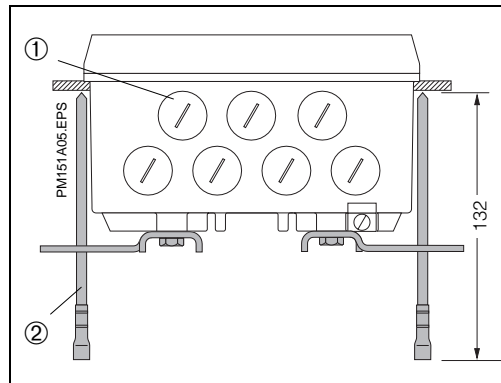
Unterseite des Feldgehäuses mit Montagemaßen sowie montierten Spanschrauben zum Schalttafeleinbau
